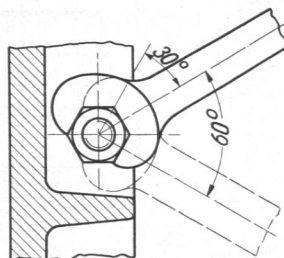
Für den Schraubenschlüssel ist genügend Platz vorzusehen.
